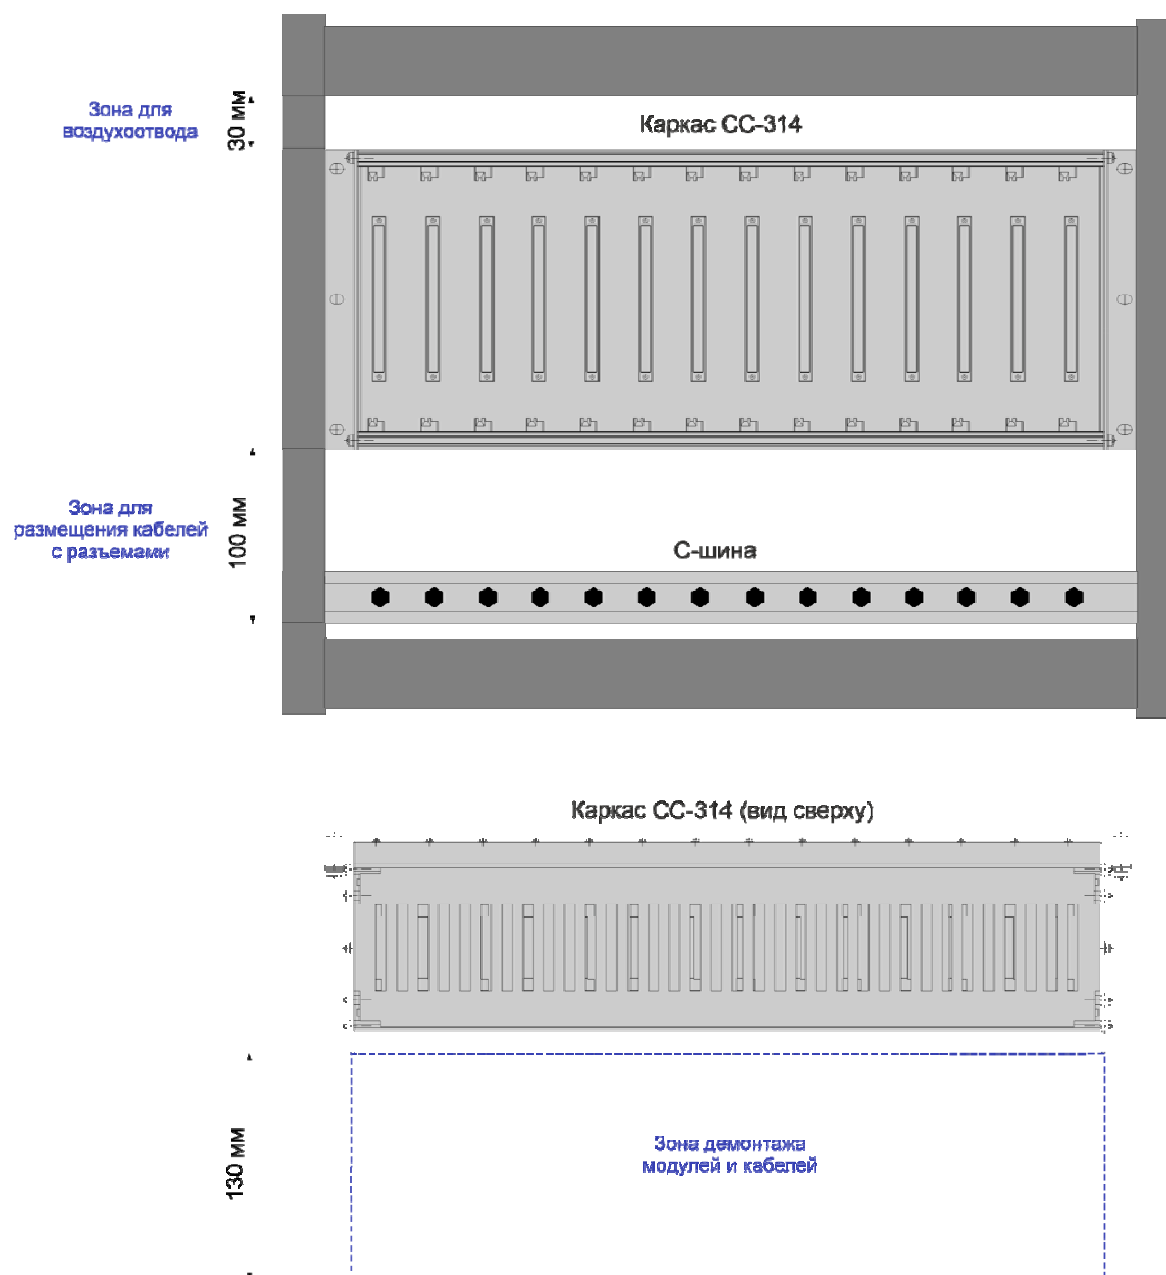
Монтаж крейта на базе каркаса CC-314 на монтажную панель шкафа (вид спереди и вид сверху)
